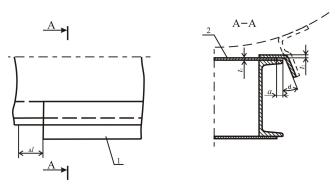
Среднее крепление котла к раме: 1 — фасонная лапа; 2 — верхняя накладка хребтовой балки
